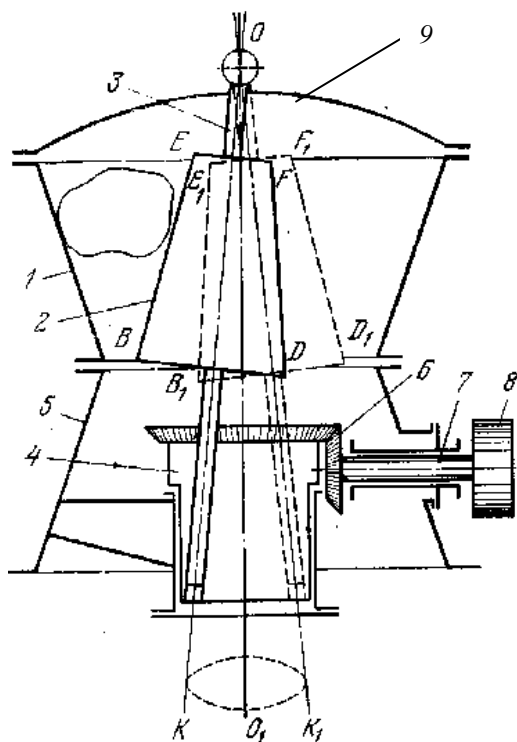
Схема конусной дробилки крупного дробления с подвешенным валом:
